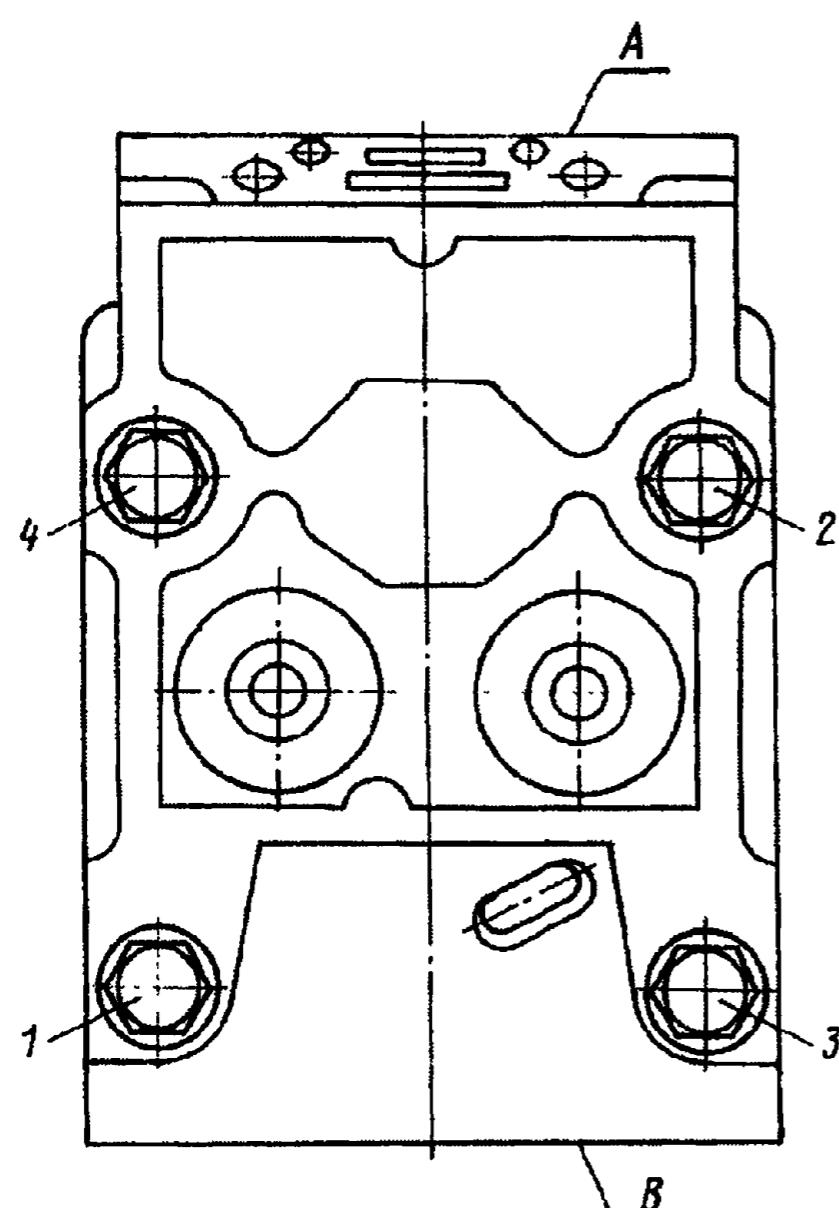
Схема затяжки болтов крепления головки цилиндра:
